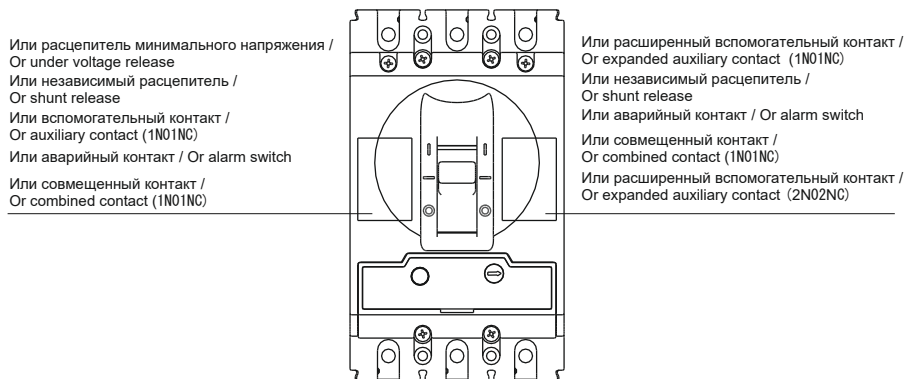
Места внутренней установки для MCCB типоразмера S /
